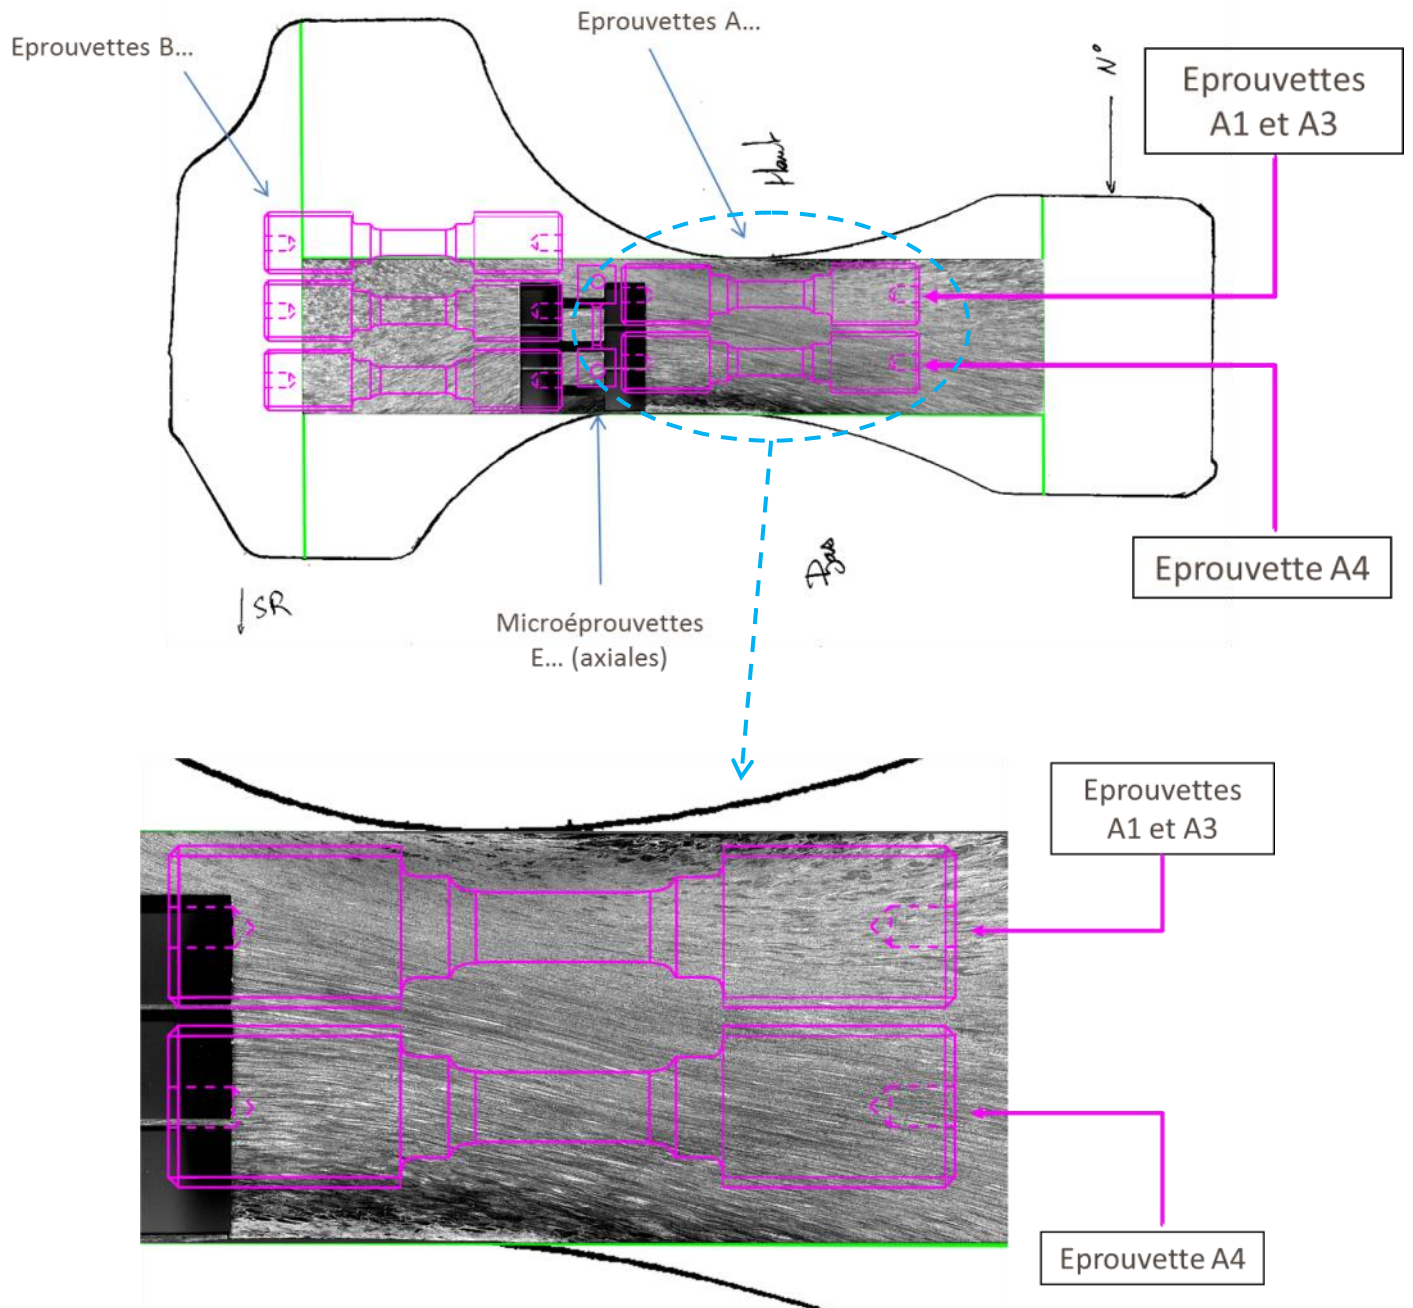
Plan de prélèvement des éprouvettes à section carrée
